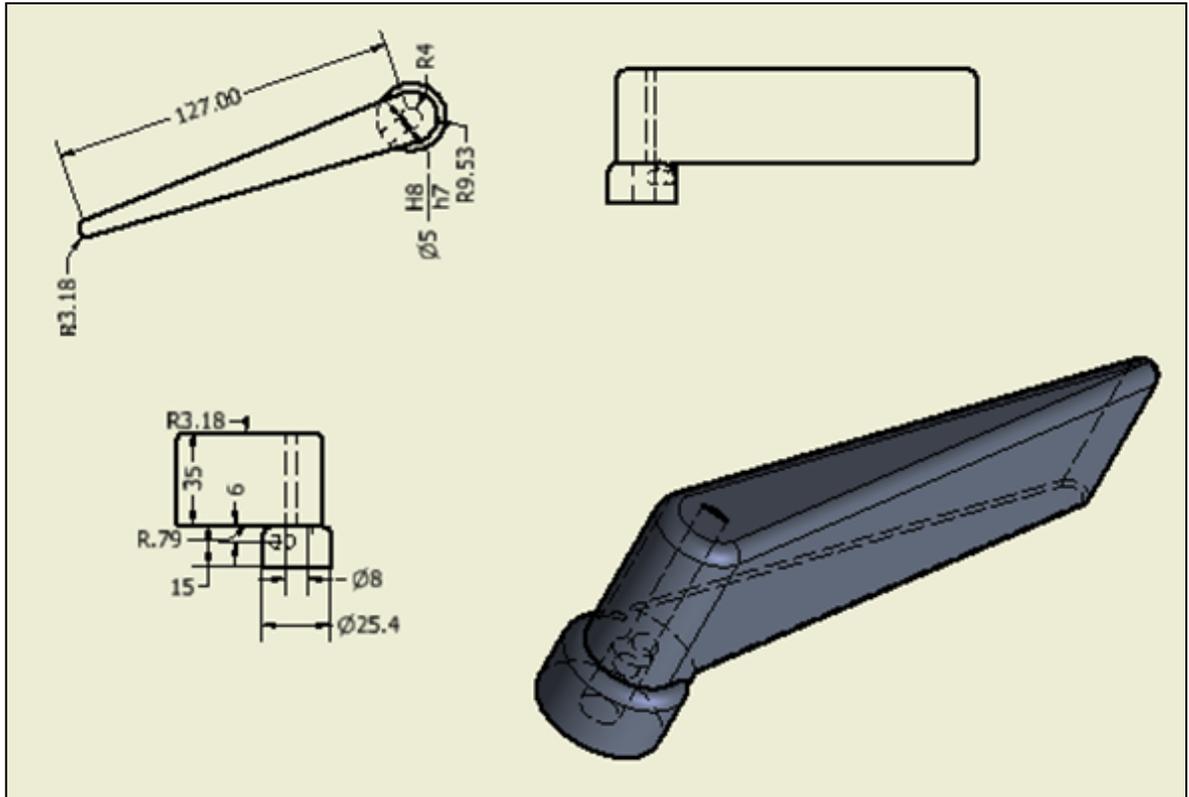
Diseño primera paleta desviadora, hacia la guía izquierda o derecha. Vista frontal.
